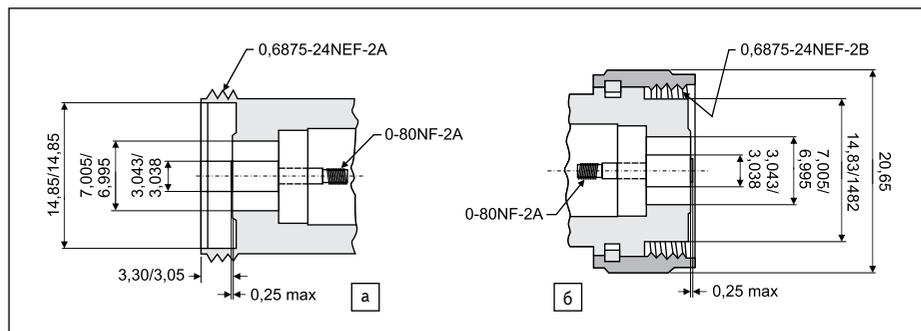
Интерфейс соединителя APC-N: а) розетка; б) вилка
